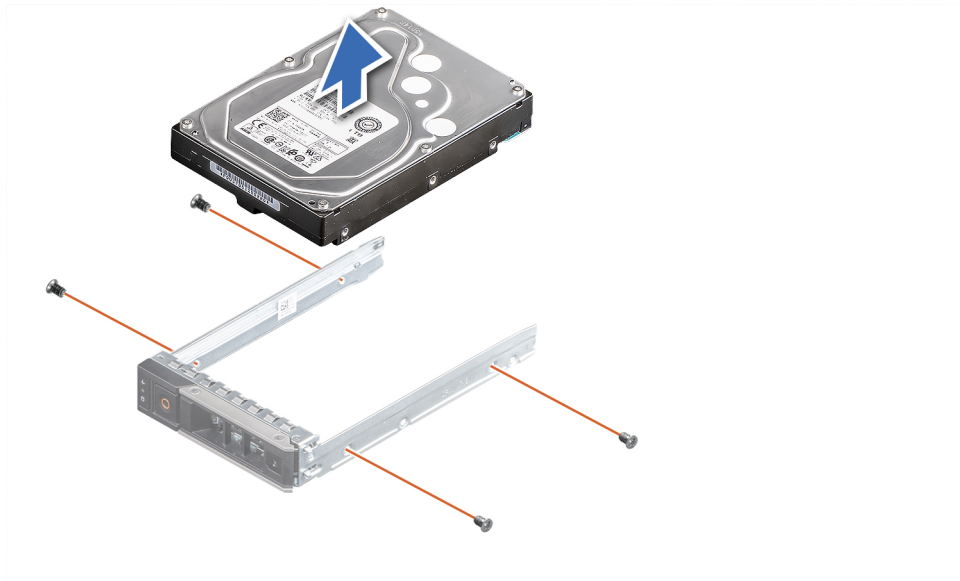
Laufwerk aus Laufwerksträger entfernen
